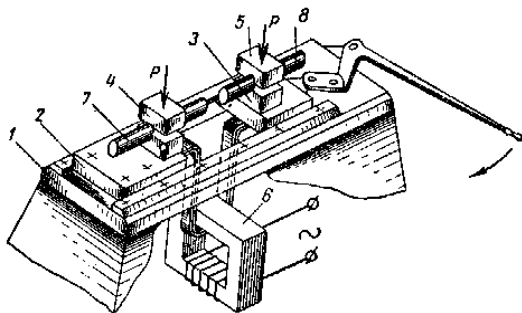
Схема машины для стыковой контактной сварки
